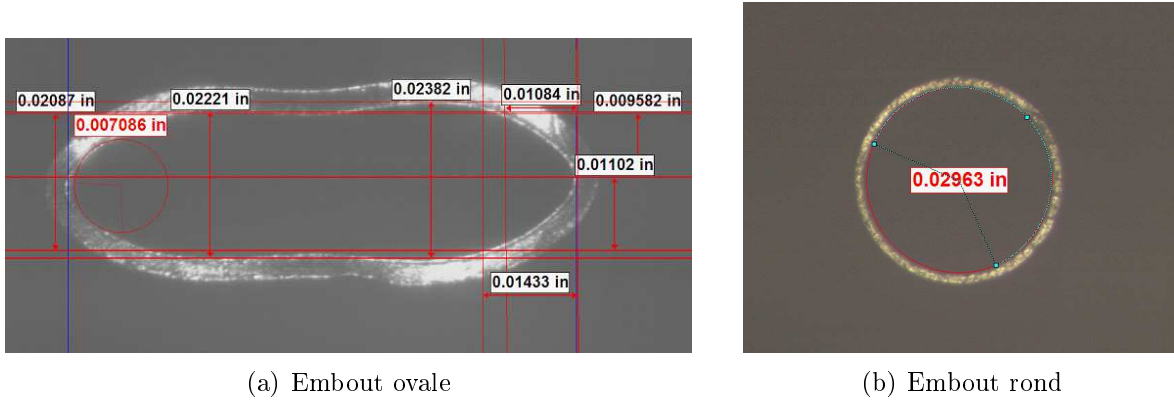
Mesure au microscope des dimensions importantes des embouts
